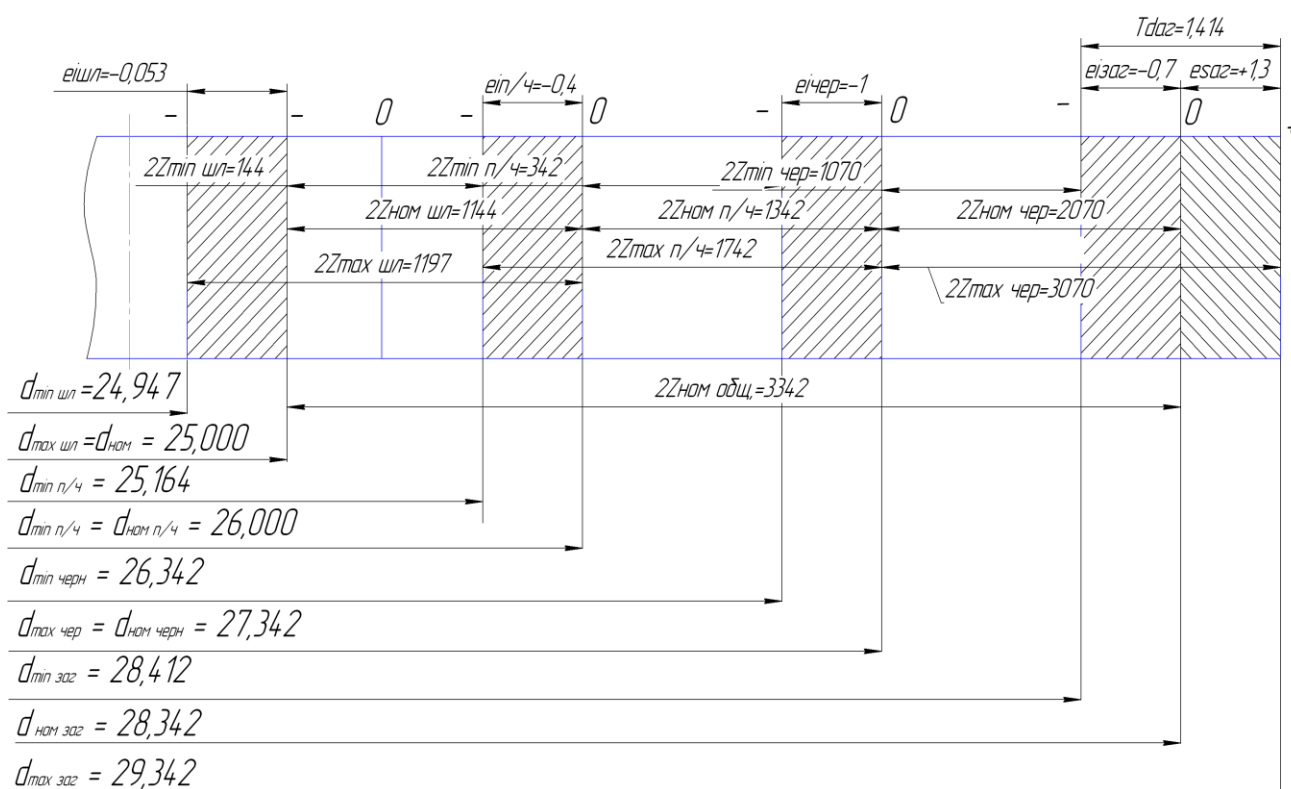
Схема расположения припусков и допусков
